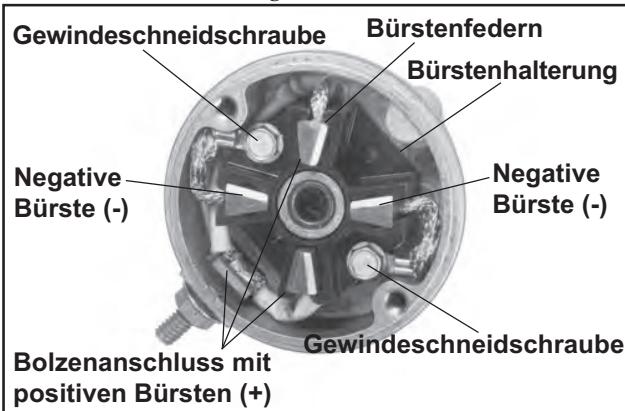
Endkappe Umschalter Typ "A" mit Bürsten.
